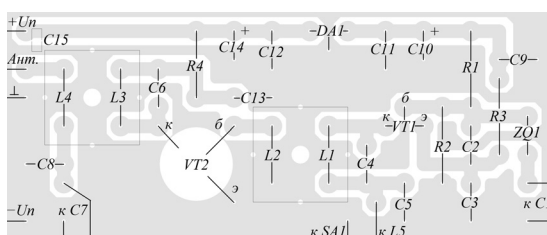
Эскиз монтажной платы QRPP-передатчика. Вид со стороны установки деталей
